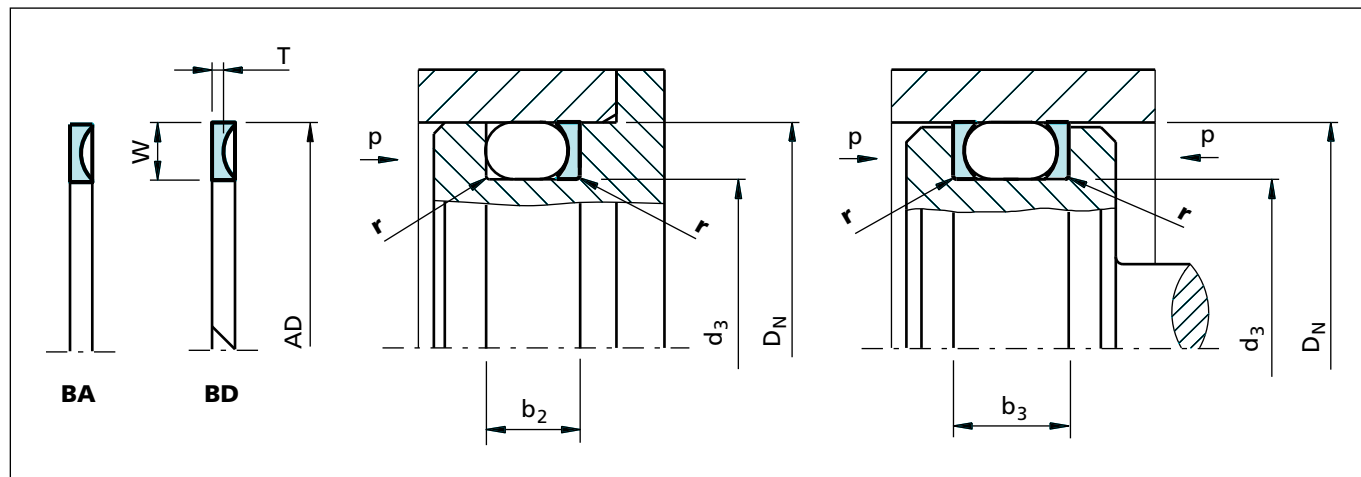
Einbauzeichnung außendichtend, konkave Stützring Bauformen
